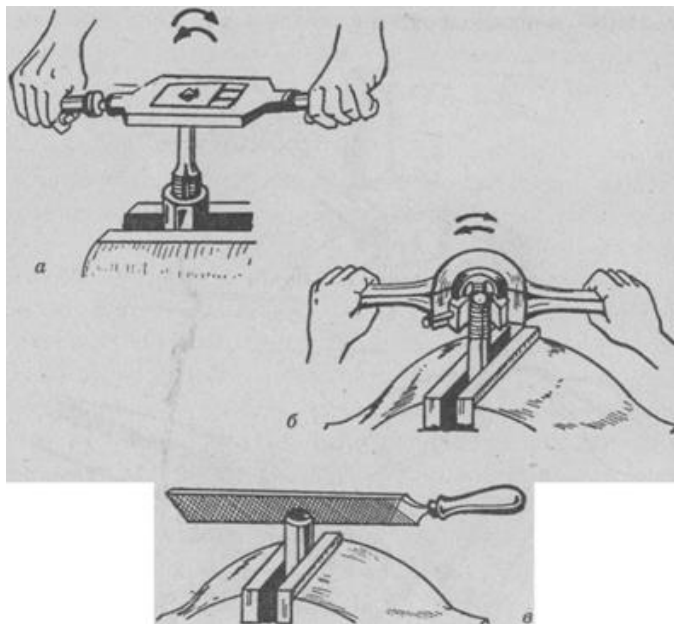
Приемы нарезания резьбы: а — внутренней резьбы с помощью метчика; б, в — опиливание торца металлического прутка и нарезание резьбы с помощью плашки и воротка.
